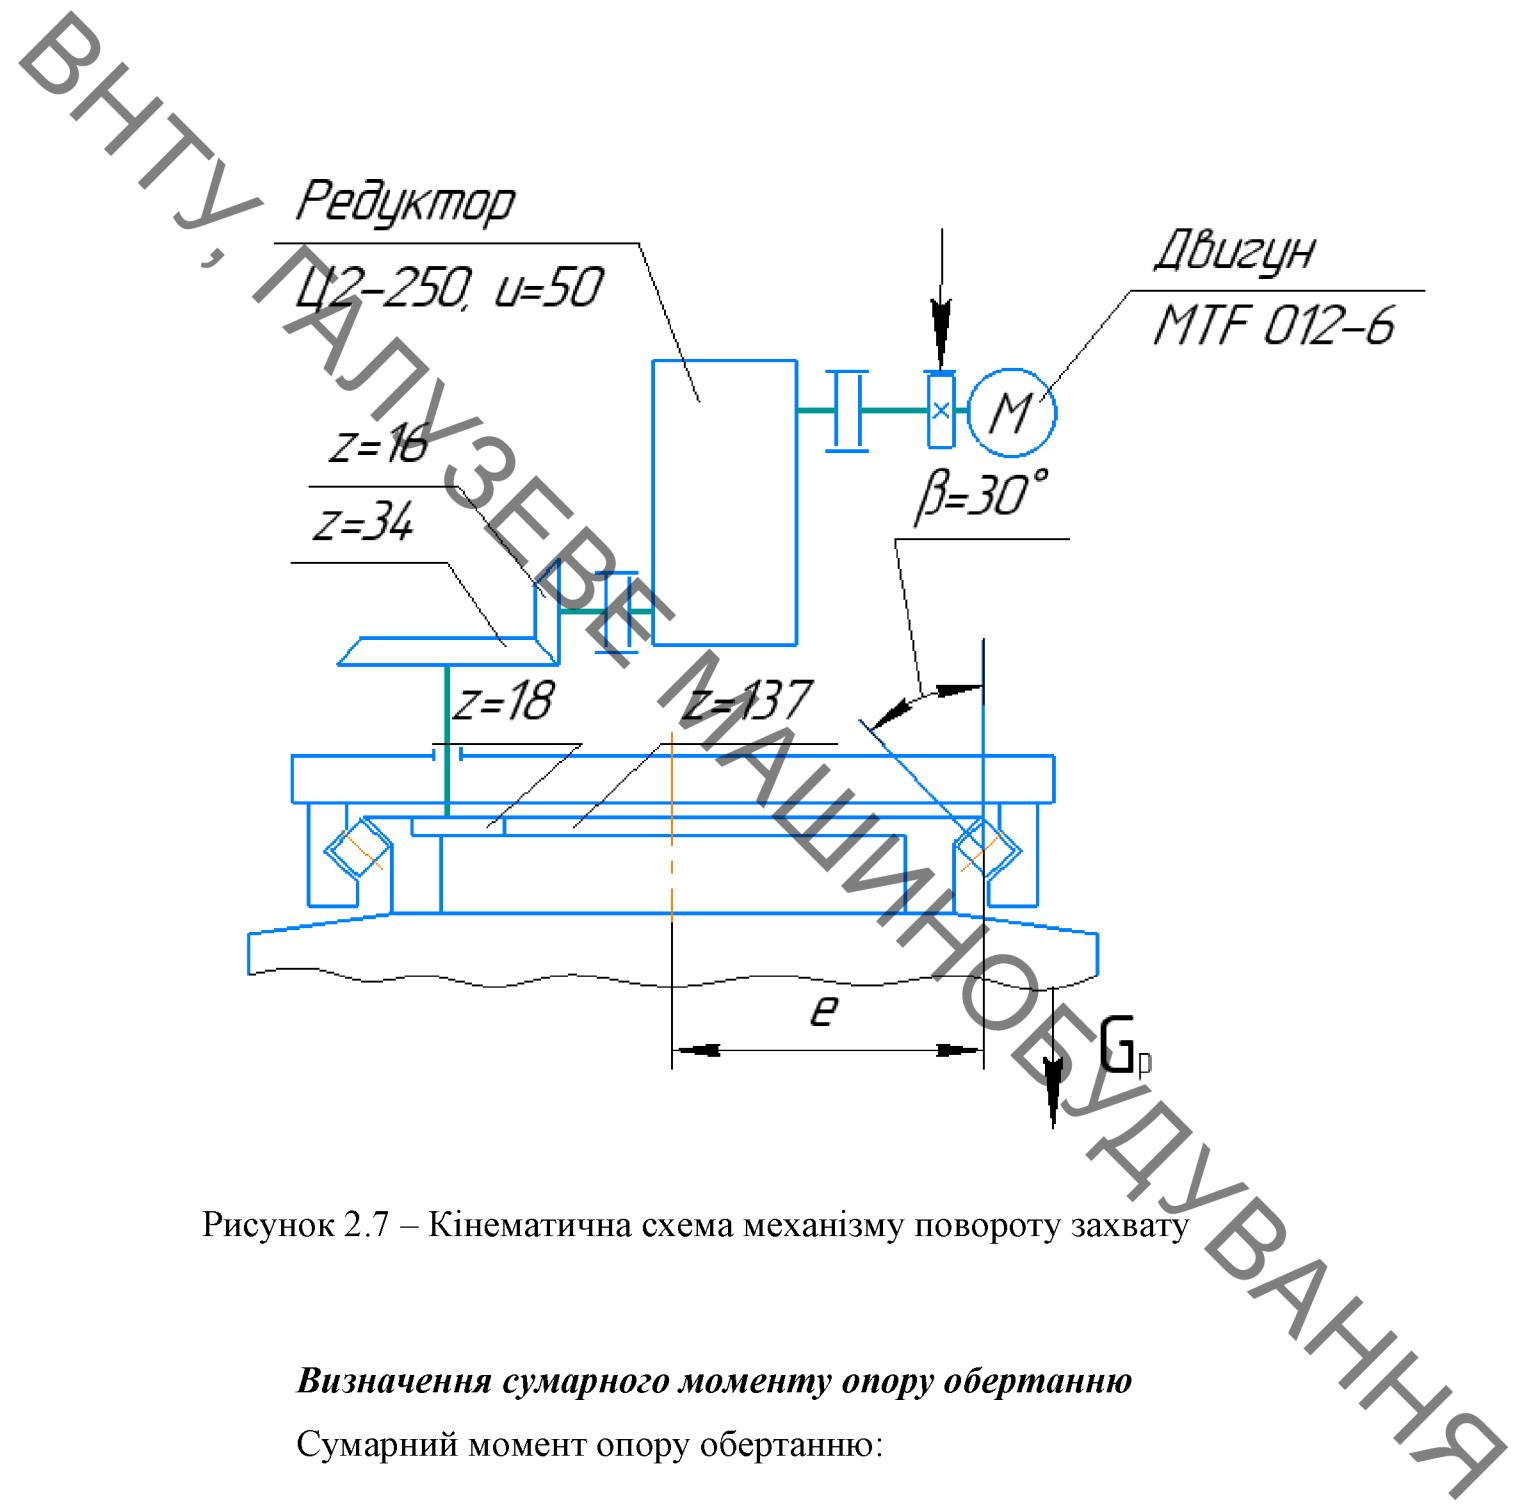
Кінематична схема механізму повороту захвату
